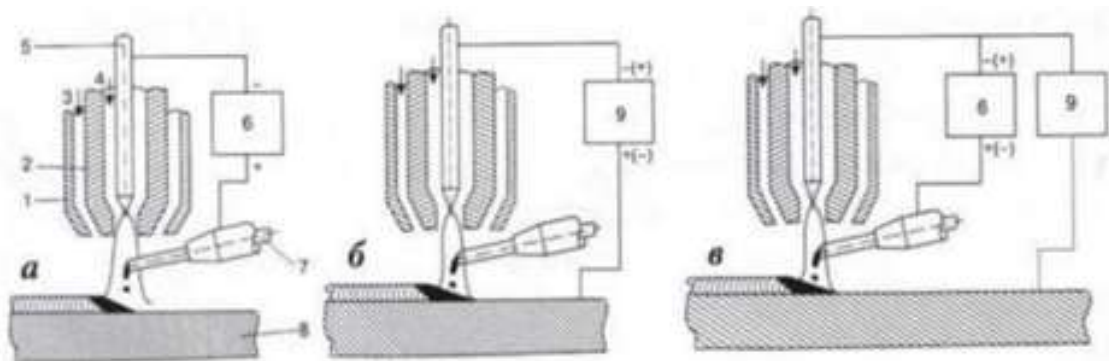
Схеми плазмового наплавлення з присадкою одного дроту:
